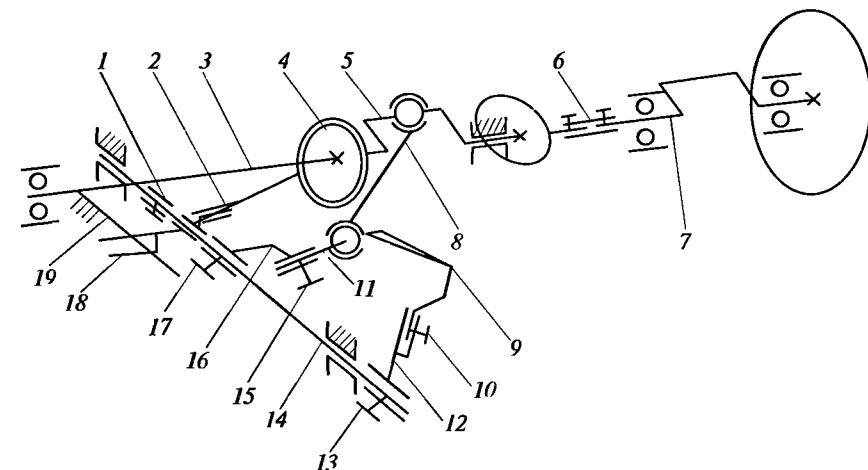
Кинематическая схема механизма петлителя швейной машины класса 1276
